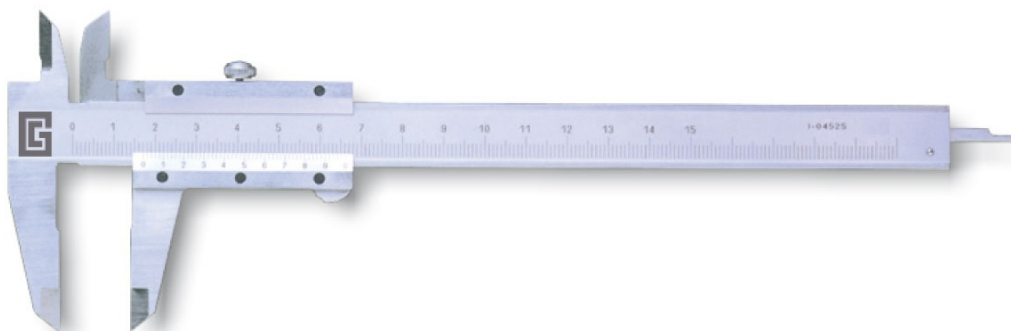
Общий вид штангенциркулей типа ШЦ-I.
